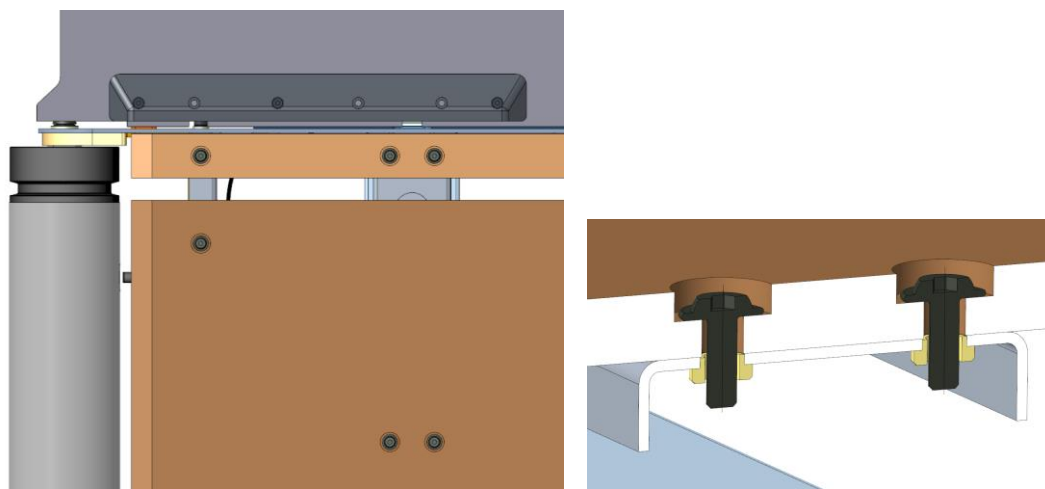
Sistema di fissaggio del telaio al pianale
